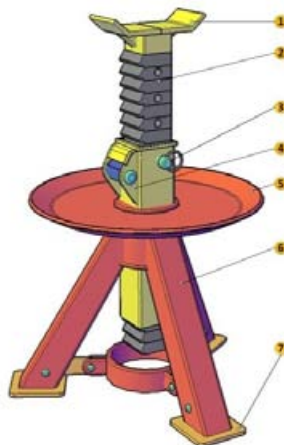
Конструкция страховочной стойки с регулируемой высотой подъема: 1) опорная площадка; 2) зубчатая рейка; 3) страховочный фиксатор; 4) храповой механизм; 5) тарелка для крепежа; 6) опорные стойки; 7) башмаки
